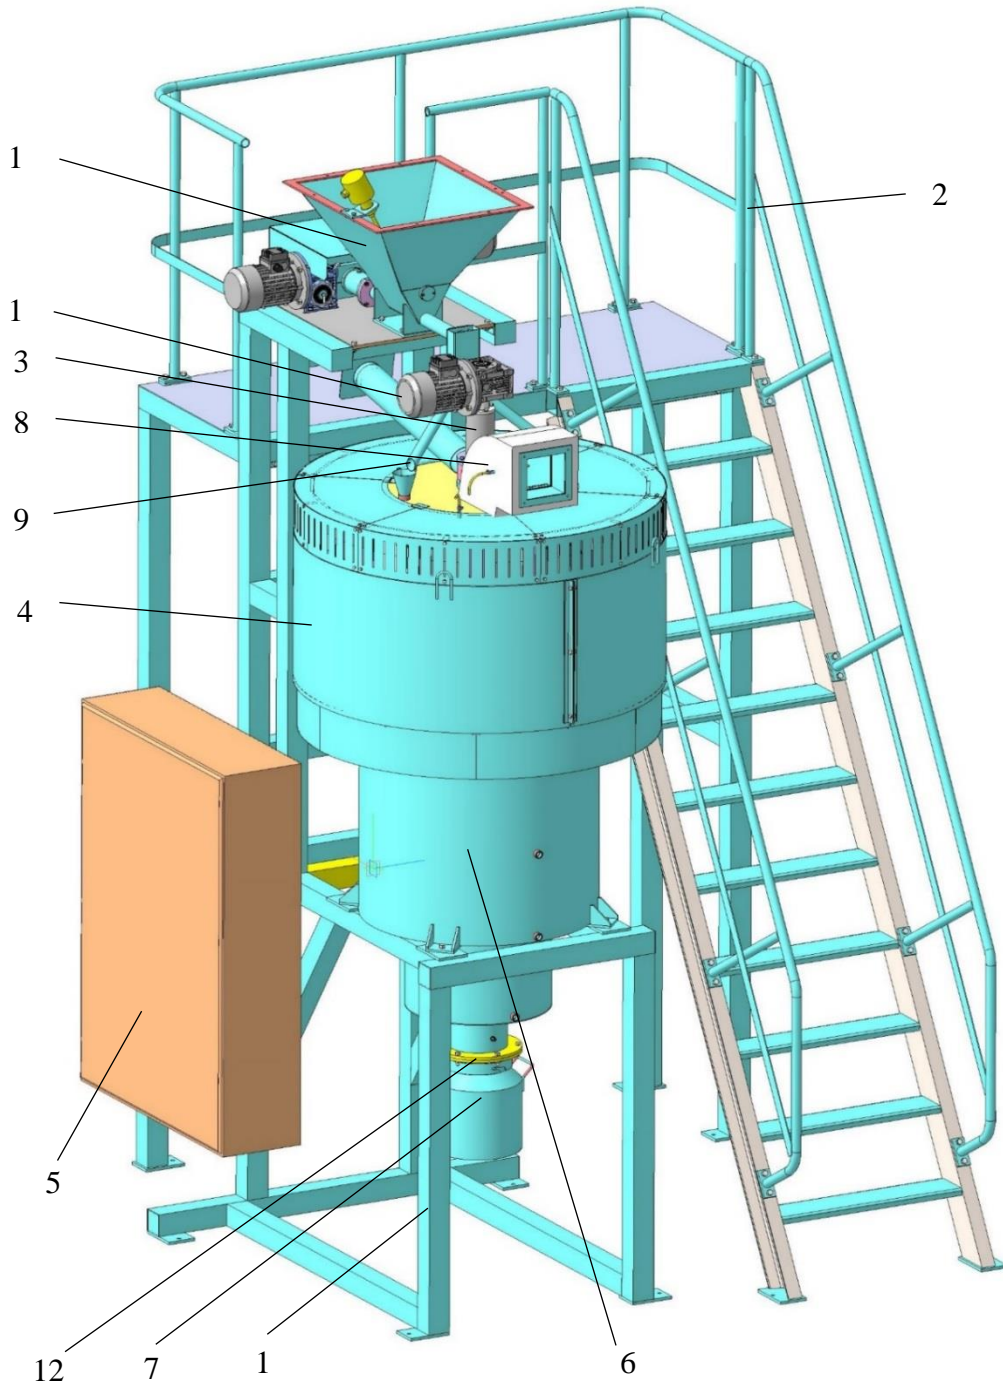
Усовершенствованный центробежный реактор барабанного типа.
